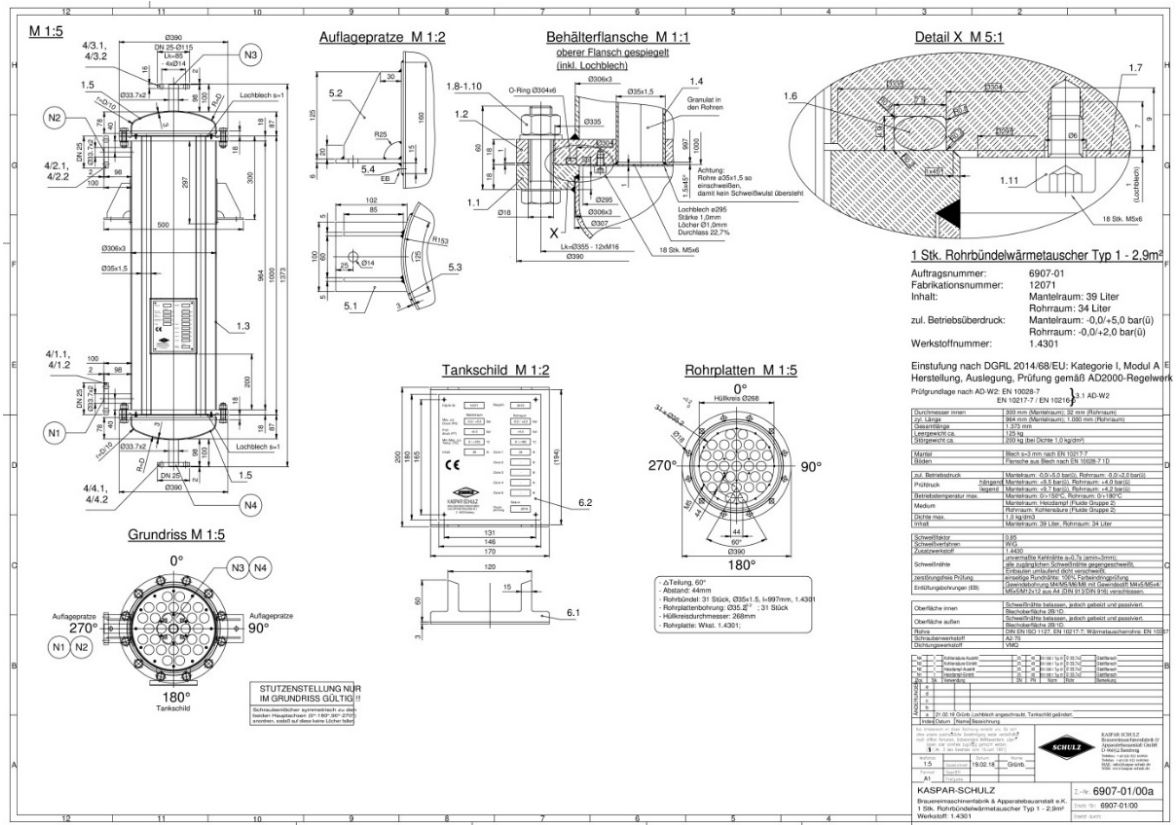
Ausgearbeiteter Rohrbündelwärmetauscher DN32.
